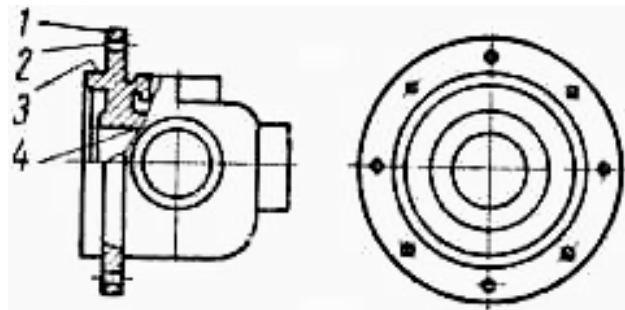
Корпус, имеющий круглый фланец и центрирующий выступ
